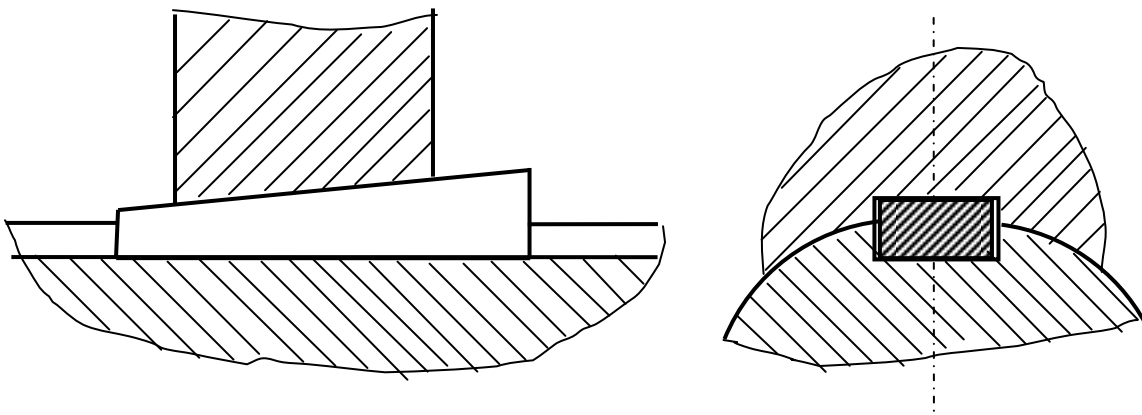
Схема з'єднання клиновою шпонкою
